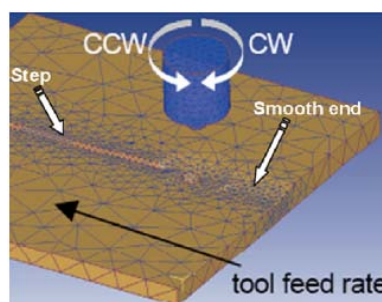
Esquema e condições fronteira da ferramenta de soldadura
